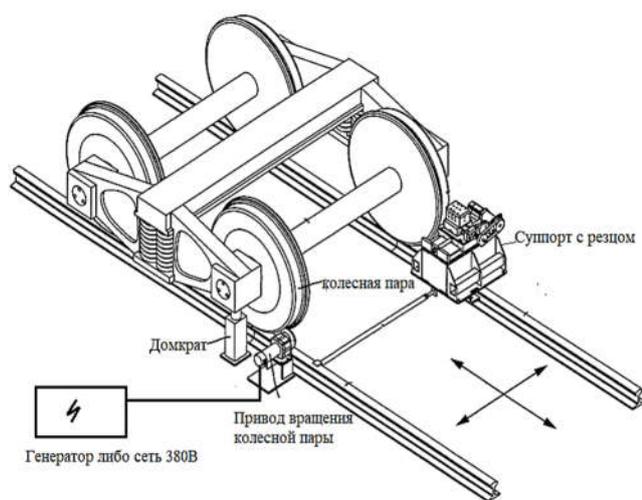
Схема мобильной установки для обточки колесных пар без выкатки из-под вагона [10]
